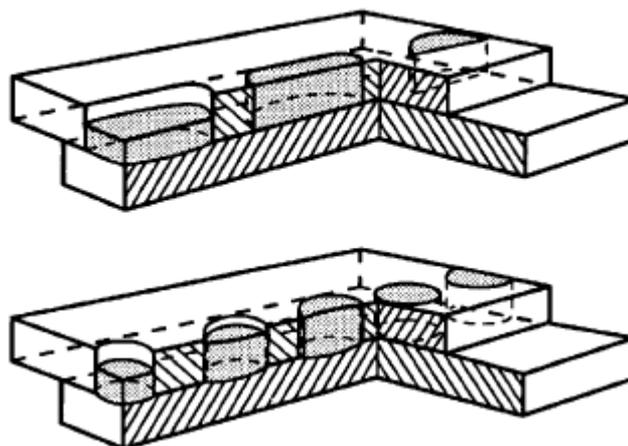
Soldaduras de Tapón y de Agujero
